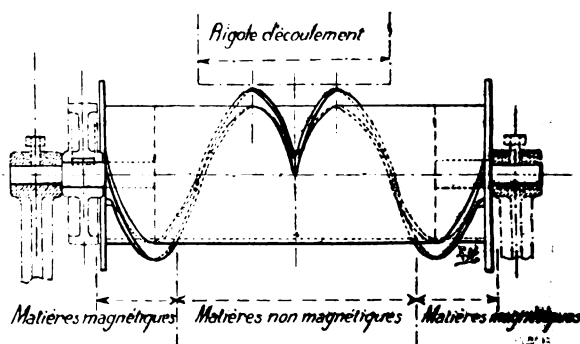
Tambour électromagnétique à cannelure Siemens-Schuckert).
